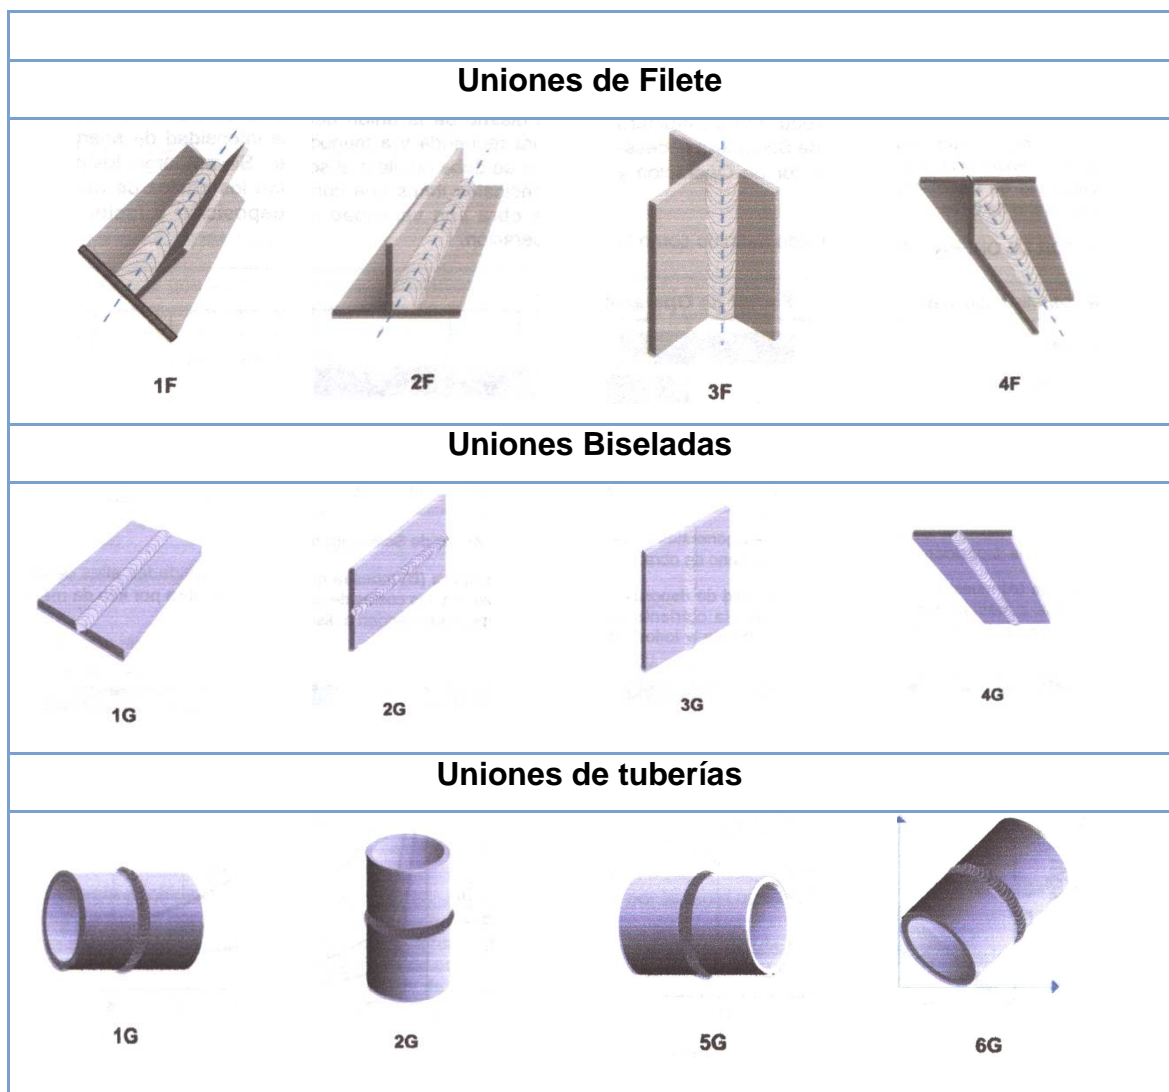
POSICIONES DE SOLDADURA
